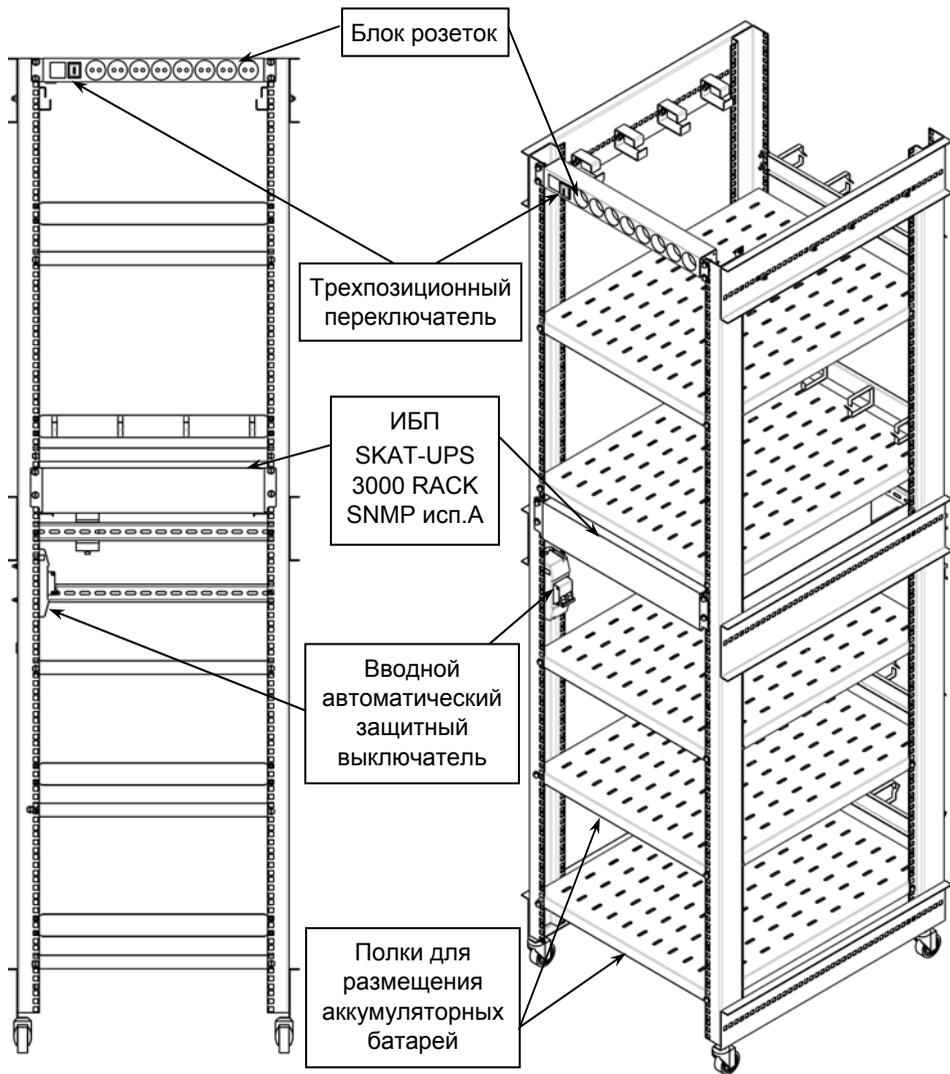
общий вид изделия спереди, без оболочки, с установленным ИБП
